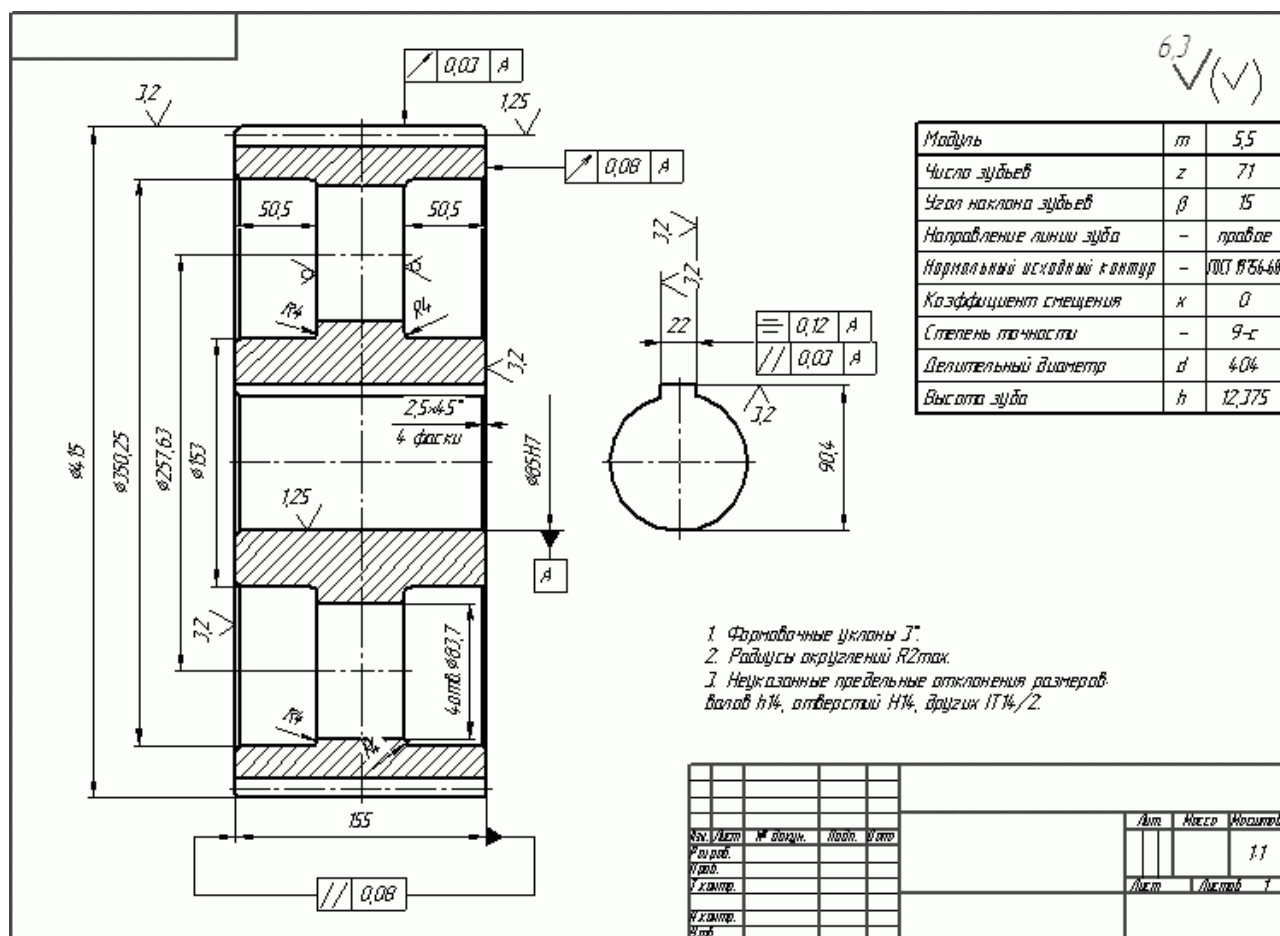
Детализировочный чертеж зубчатого колеса
